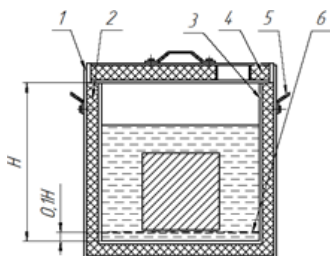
Ванна для охлаждения деталей путем погружения их в жидкий азот: 1 – кожух; 2 – теплоизоляция; 3 – внутренняя часть ванны; 4 – крышка; 5 – ручка; 6 – решетка;
